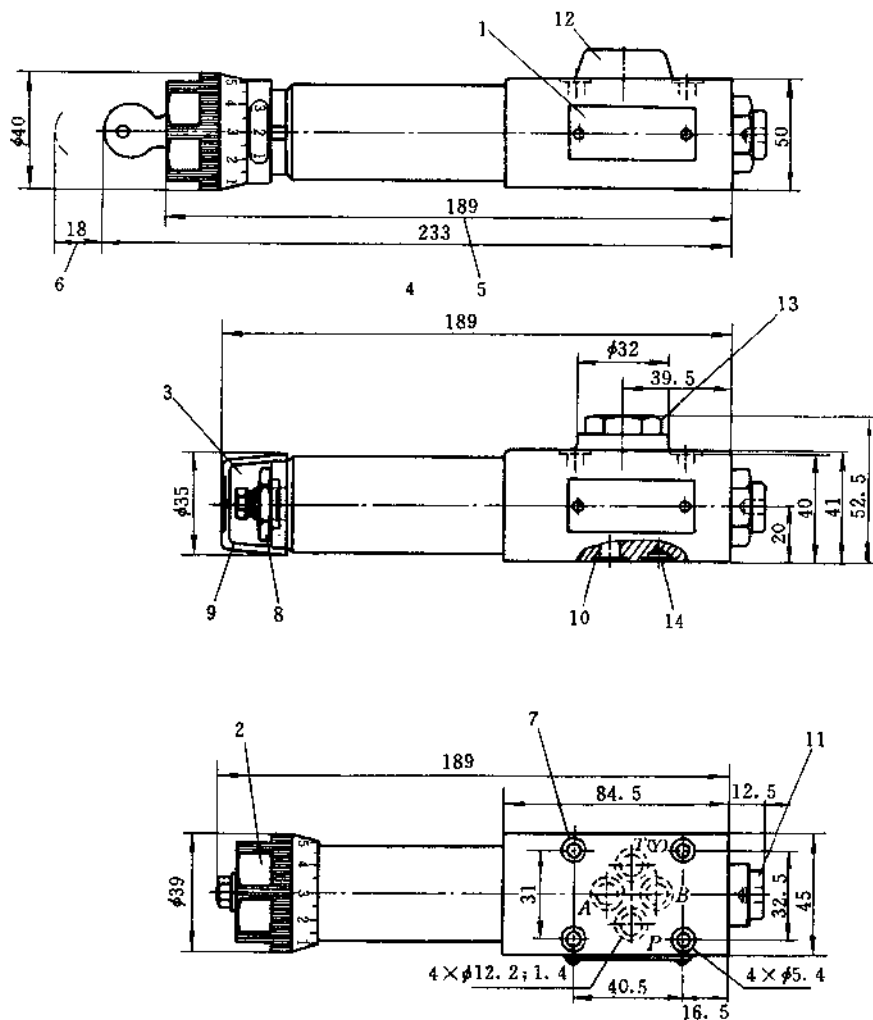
DR6DP 型直动式减压阀外形尺寸图
